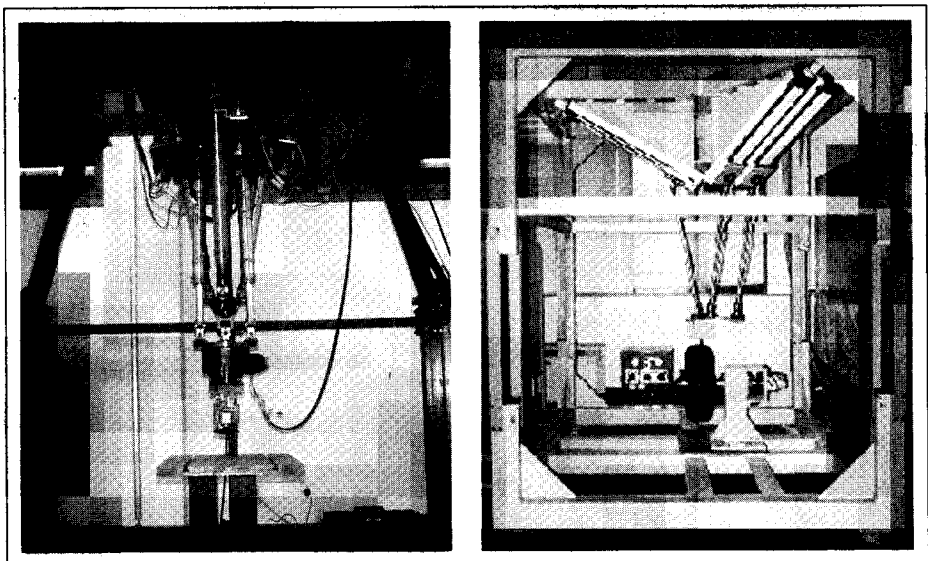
Double Parallel Machine and Tire carving Hexapod Machine
